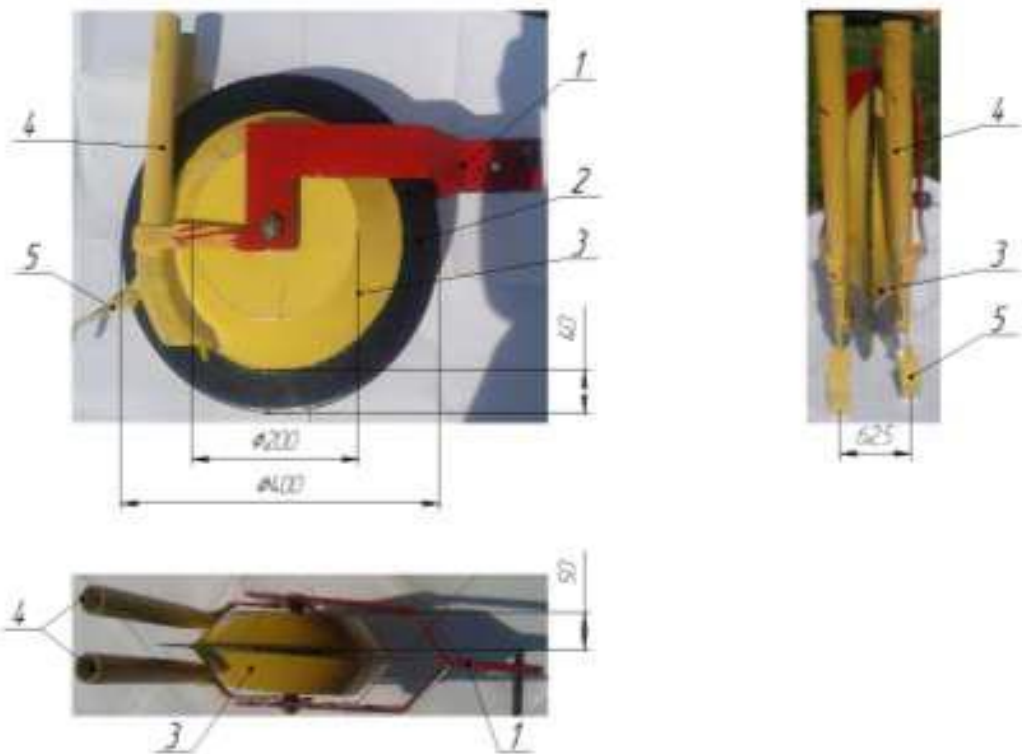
Новий макетний зразок однодискового сошника із зовнішніми симетричними ребрами-борозноутворювачами (варіант 2): 1 – корпус сошника; 2 – диск; 3 – ребра-борозноутворювач; 4 – насіннепровід; 5 – клапан насіннепровода.
